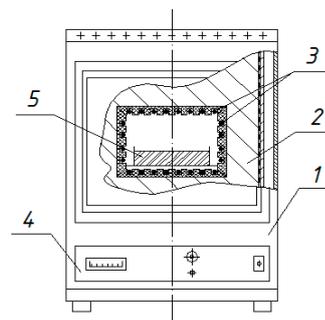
Схема печи: 1 – корпус; 2 – теплоизоляция; 3 – нагреватель; 4 – блок управления; 5 – нагреваемая садка
